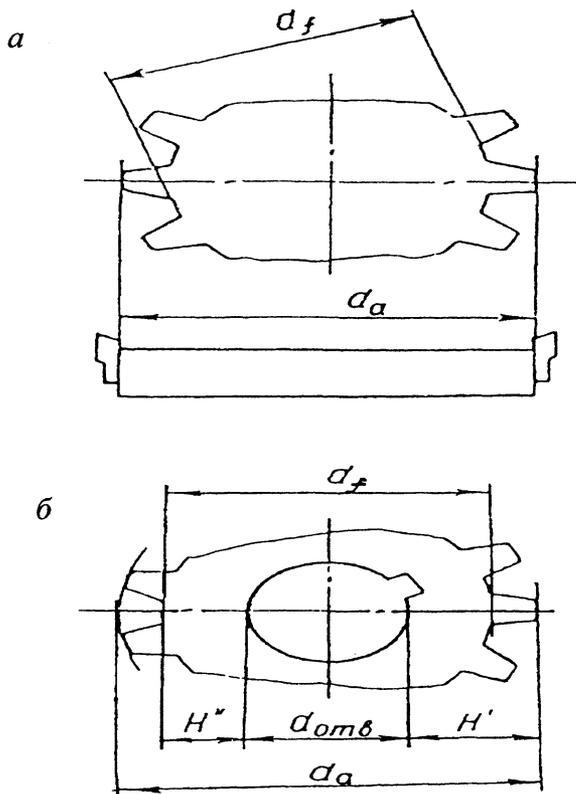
Схема обмера диаметров вершин (d_a) и впадин (d_f) зубчатого колеса: a – при четном числе зубьев (диаметры d_a и d_f измеряются штангенциркулем); b – при нечетном числе зубьев (диаметры d_a и d_f определяются по формулам $d_a = d_{отв} + 2H'$ и $d_f = d_{отв} + 2H''$)
